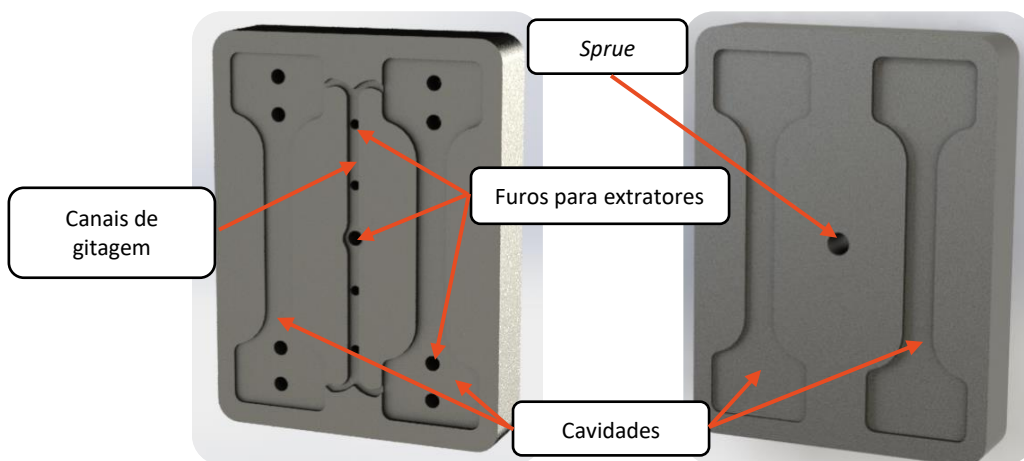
Desenhos CAD 3D das meias moldações móvel (à esquerda) e fixa (à direita) para produção de provetes.
